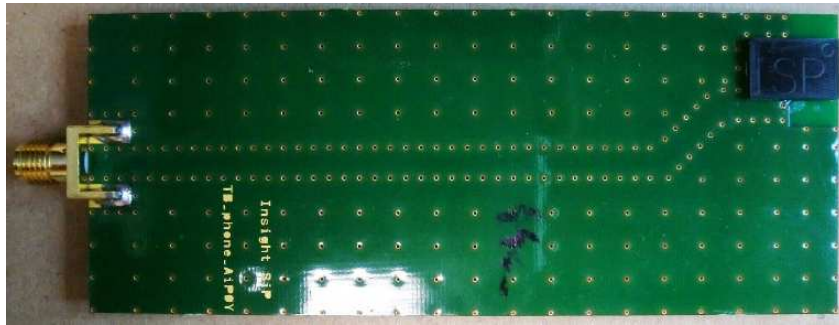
Module contenant uniquement l’antenne, soudé sur un PCB de test de type téléphone portable
